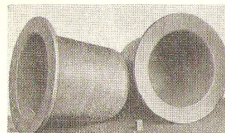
Литниковая система для отливки тигля для плавки алюминиевых сплавов.
